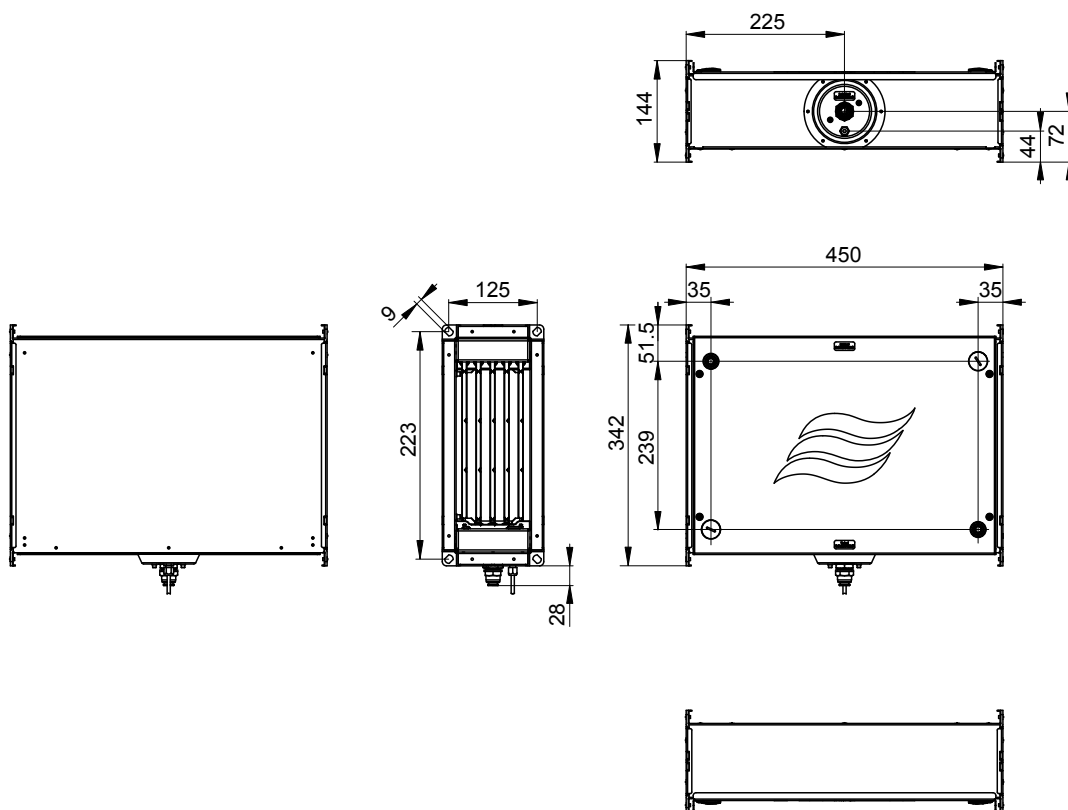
Dimensions unité d'humidification 1 kg/h (dimensions en mm)
